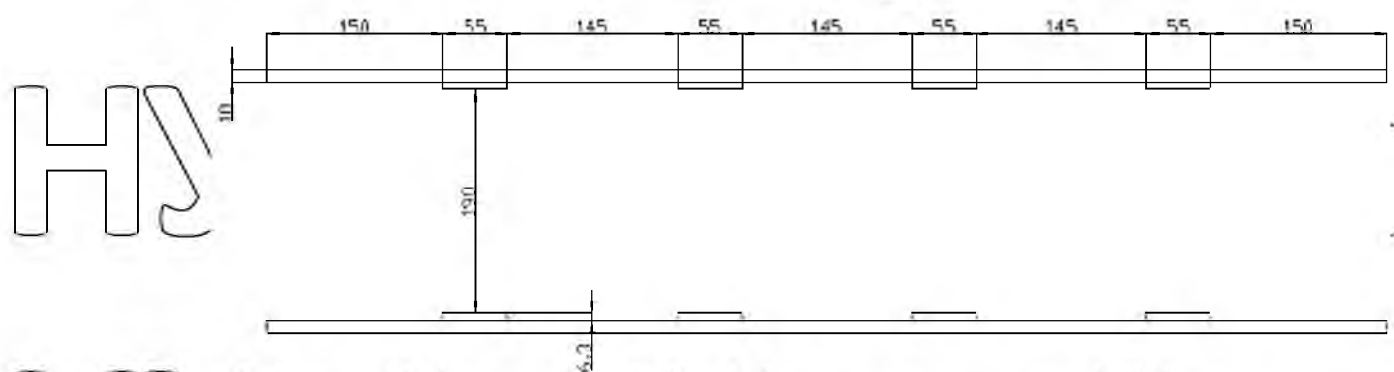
Схема пристрою для магнітної обробки картоплі
